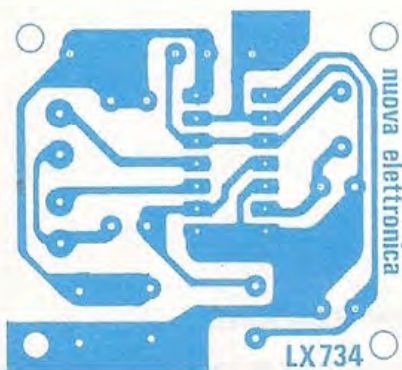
Dimensioni reali del circuito stampato richiesto per questa realizzazione.
